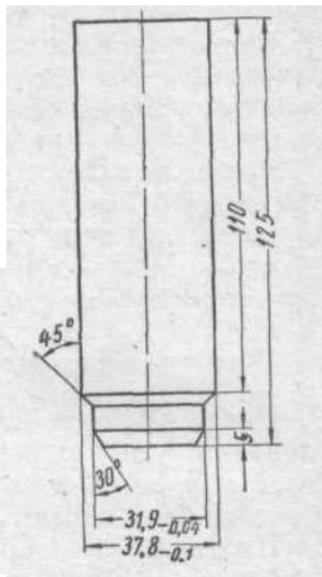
Оправка для развальцовывания трубы рулевой колонки
